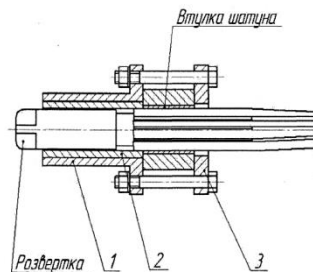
Пристрій для розвертання втулки верхньої головки шатуна
